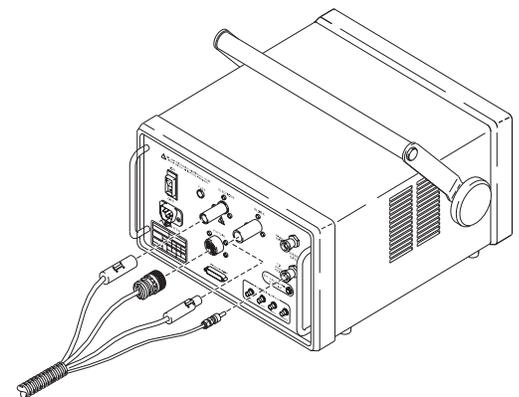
Steckverbinder des Schweißkopfes
